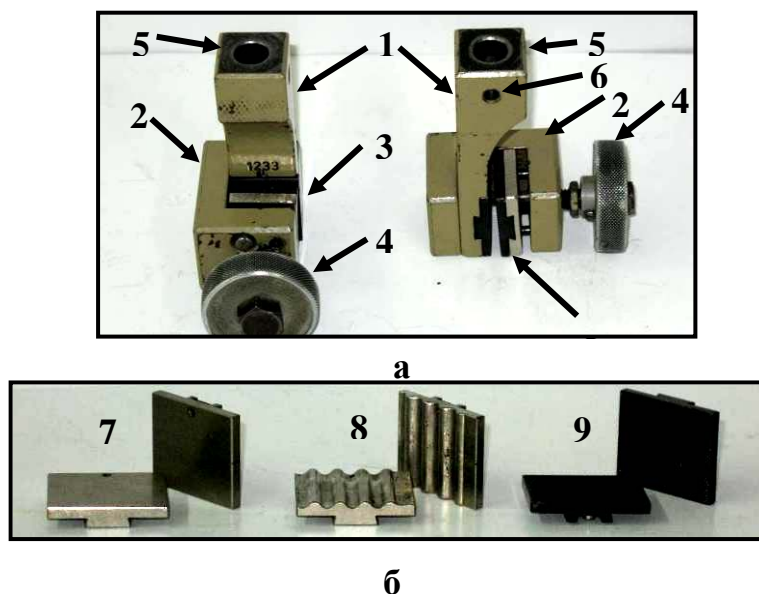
Затискувачі для випробувань конструкційних пластмас на розтяг (а) та знімні затискні губки (б): 1 – корпуси затискувачів; 2 – затискні скоби; 3 – знімні губки; 4 – затискні гвинти; 5 – отвори для з'єднання з віссю динамометра; 6 – отвори для фіксуючих штифтів; 7, 8 – губки з гладкою поверхнею та гофрами; 9 – губки з рифленою поверхнею
